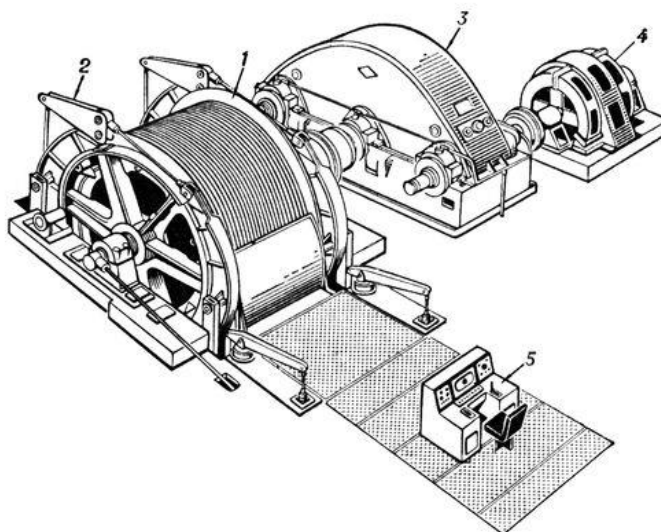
одноцилиндрический барабан; 2 — тормозное устройство; 3 — редуктор; 4 — электродвигатель
